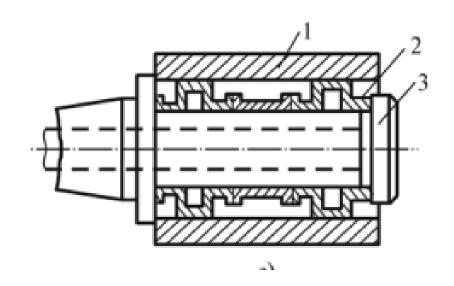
Оправка с гофрированными втулками: 1 – обрабатываемая деталь; 2 – гофрированная втулка; 3 - болт
